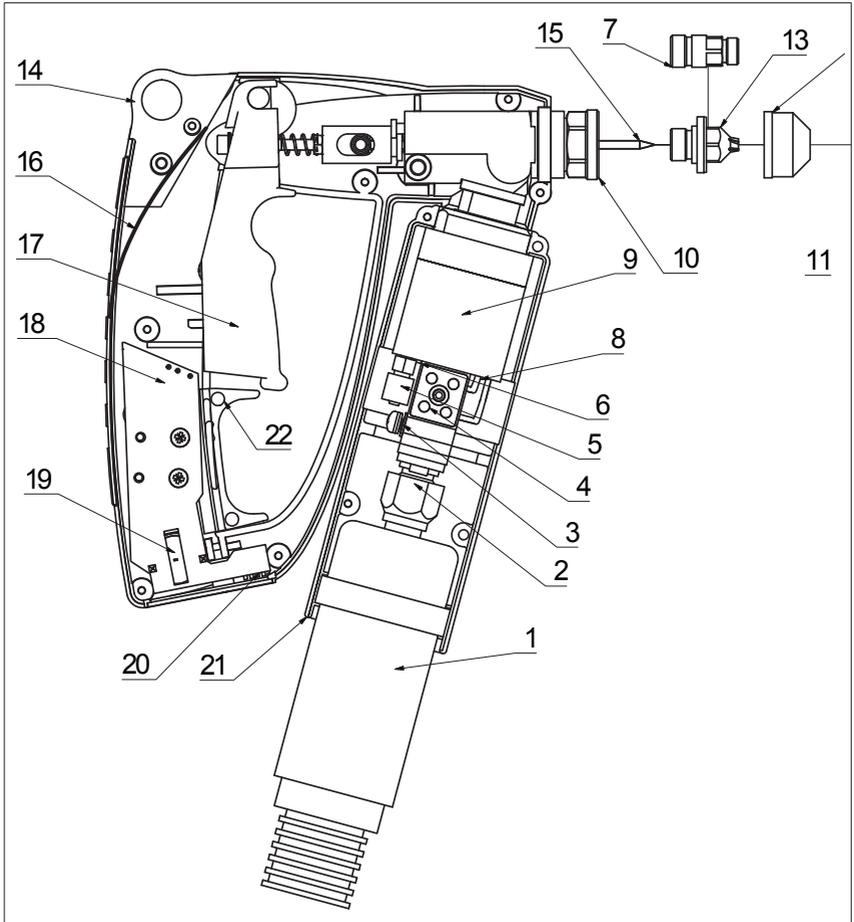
/2: Mechanischer Aufbau des Handauftragsgerätes Version Spray
